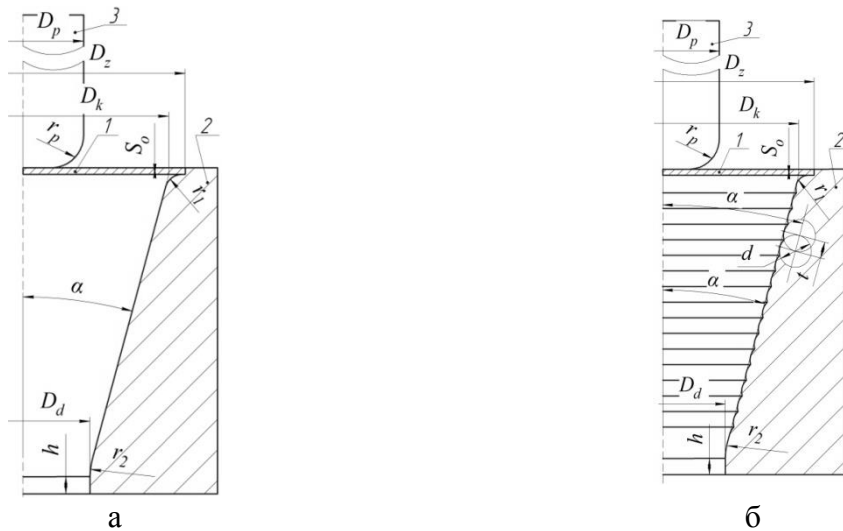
Схема комбінованого витягування в одноконусній матриці:
